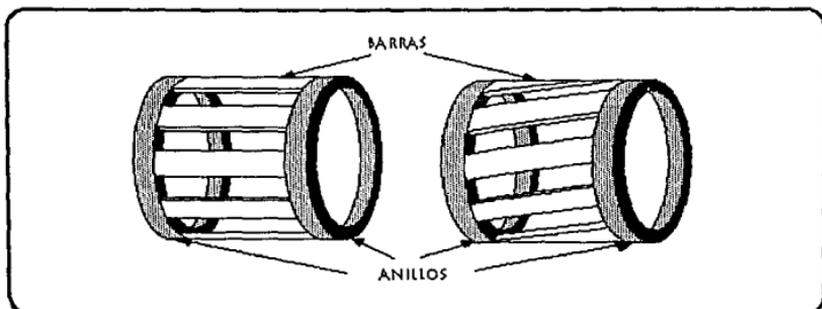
PRINCIPIO CONSTRUCTIVO DEL ROTOR TIPO JAULA DE ARDILLA. LAS BARRAS PUEDEN SER HORIZONTALES O INCLINADAS.
